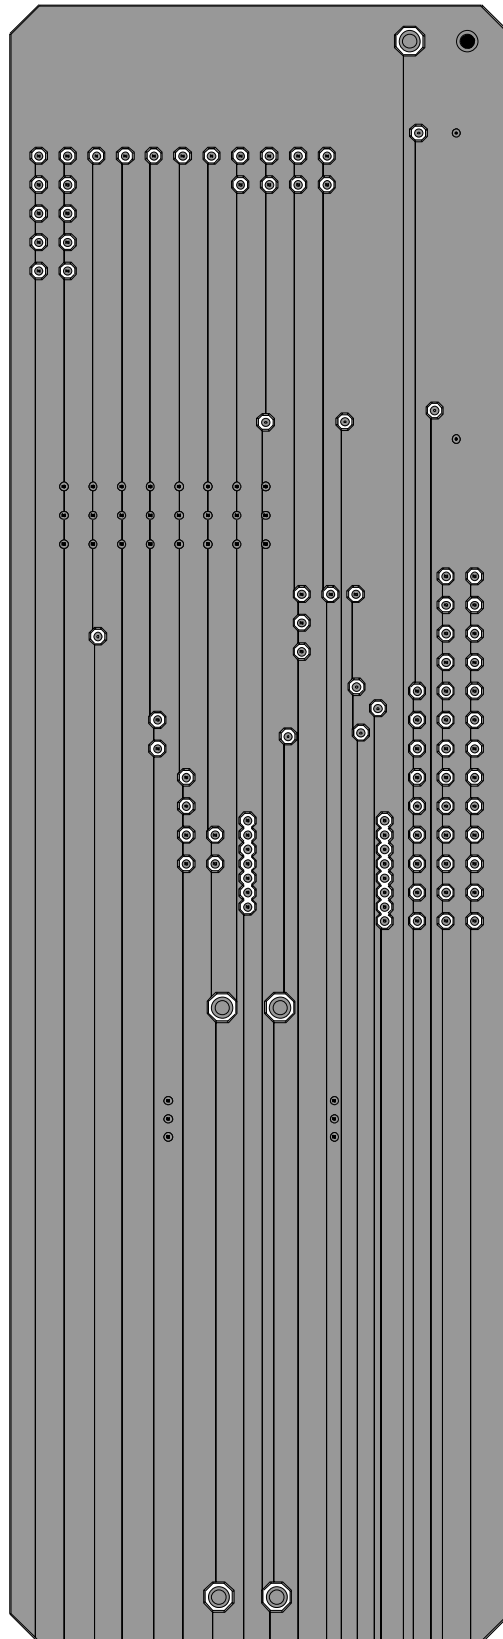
+7,3V-omvandlare lager 2 helt jordplan
